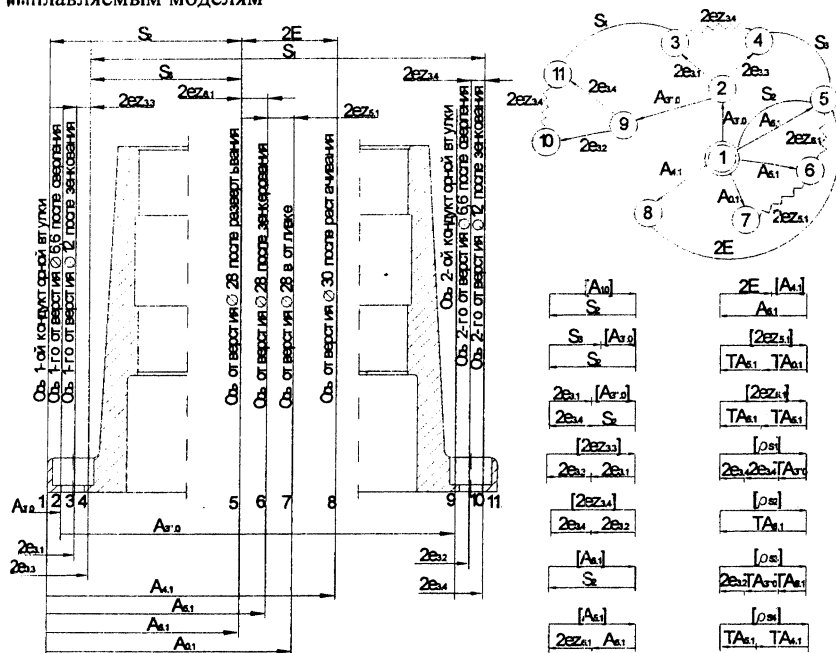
Схема обработки, граф и схемы размерных цепей корпуса
